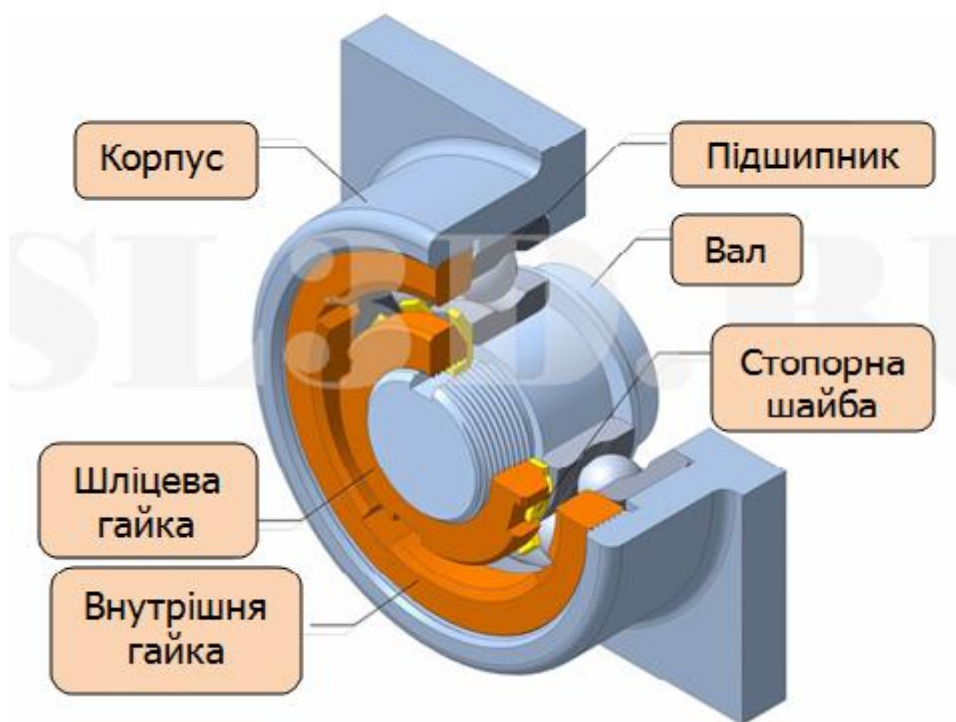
Установка підшипника з затягуванням зовнішньої обойми гайкою і упором в буртик корпуса
